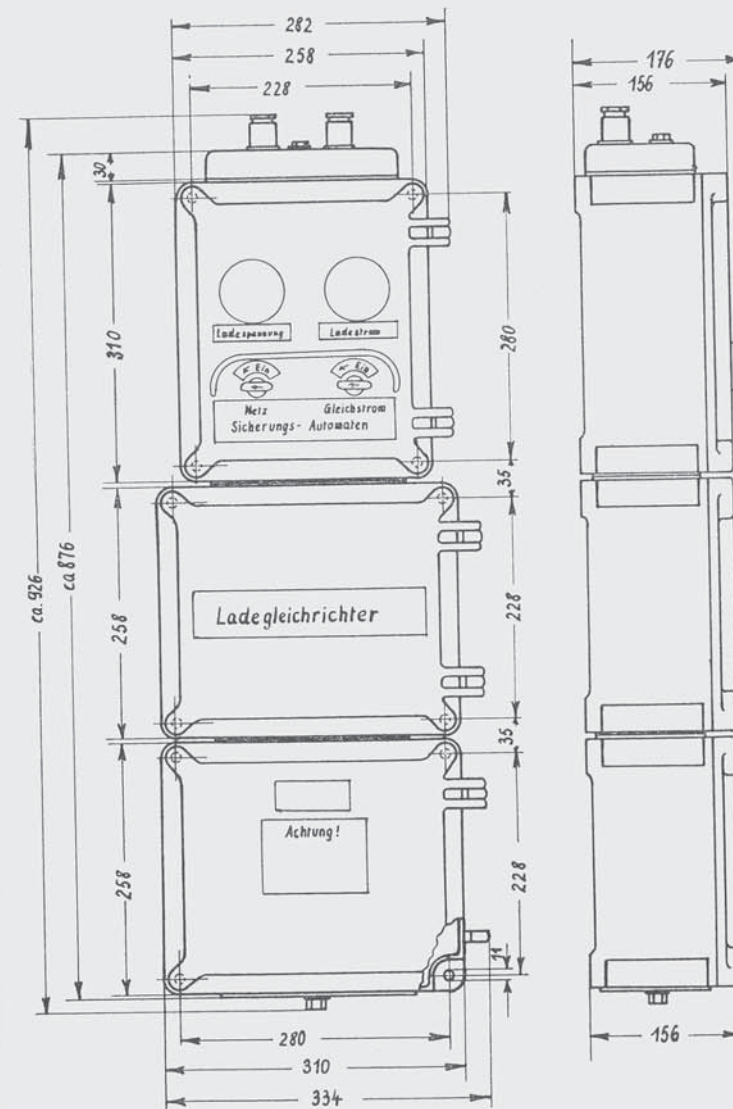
Ladegleichrichter für 5 A, Maßbild
